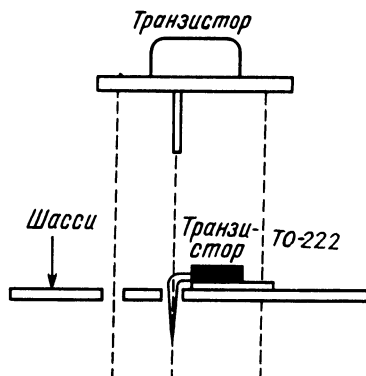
TO-220 - аналог корпуса TO-3.
